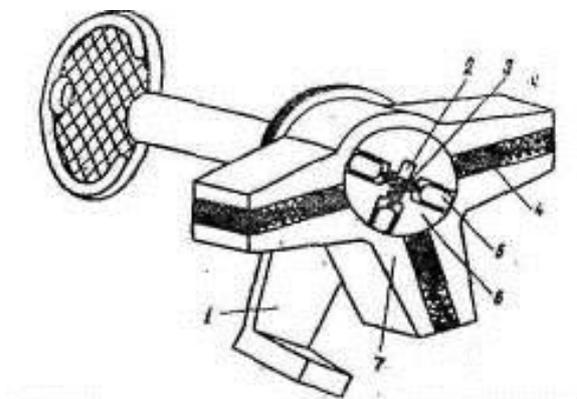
Устройство цилиндрического механизма с тремя рядами штифтов: 1 - поводок; 2 - скважина для ключа; 3 - ключ; 4 - штифт корпуса; 5 - штифт цилиндра; 6 - цилиндр; 7 - корпус
